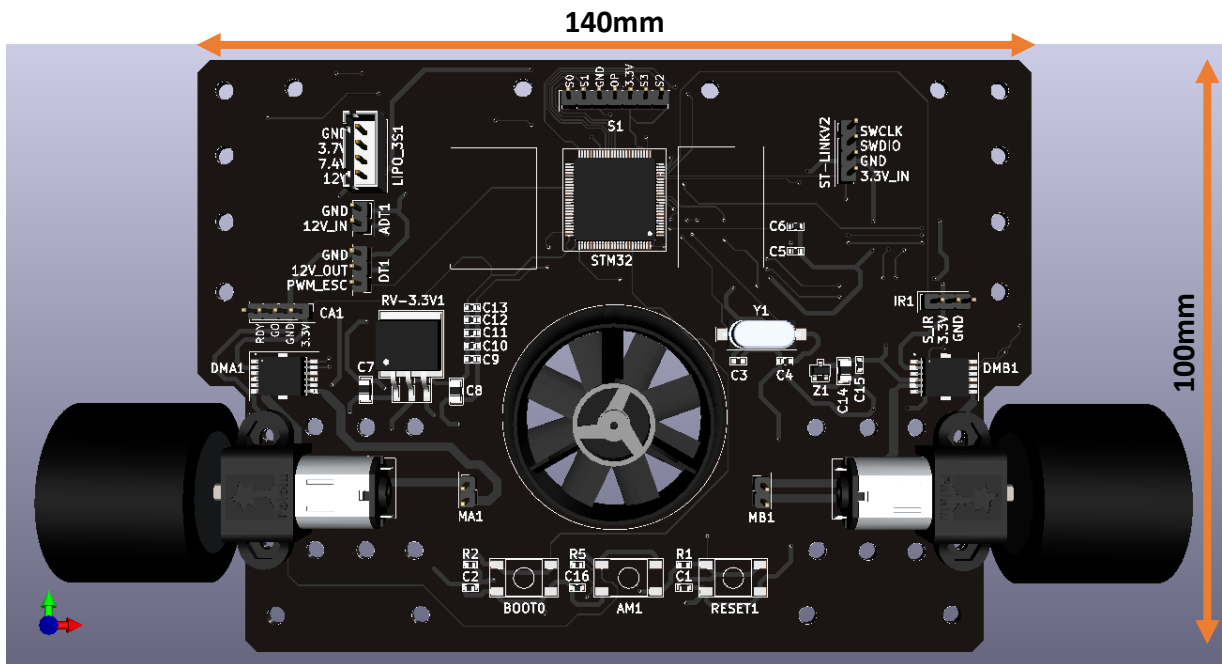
Vista Frontal en 3D de la PCB del Robot Seguidor de Línea en KiCad.
